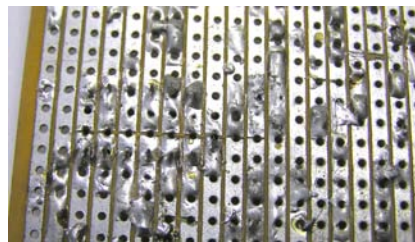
Detalle de soldaduras y cortes en una placa de tiras usada varias veces
